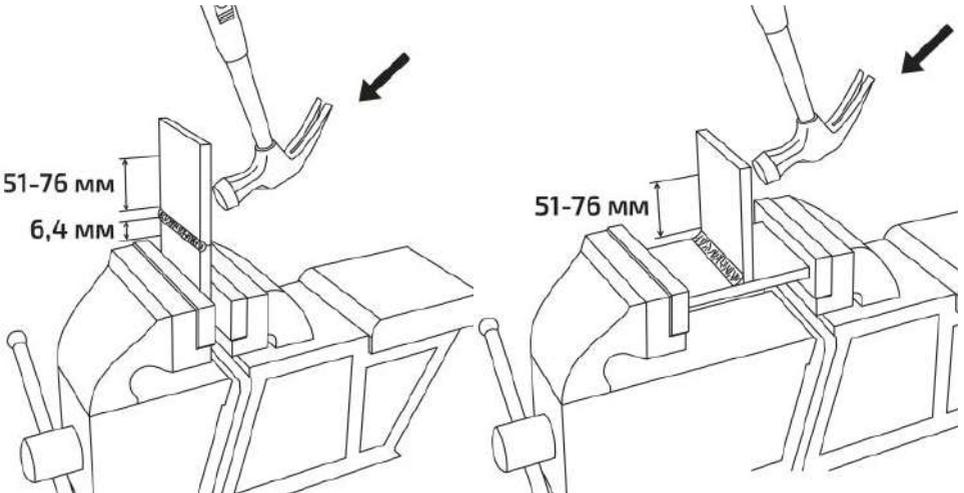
Проверка на прочность сварного соединения.
